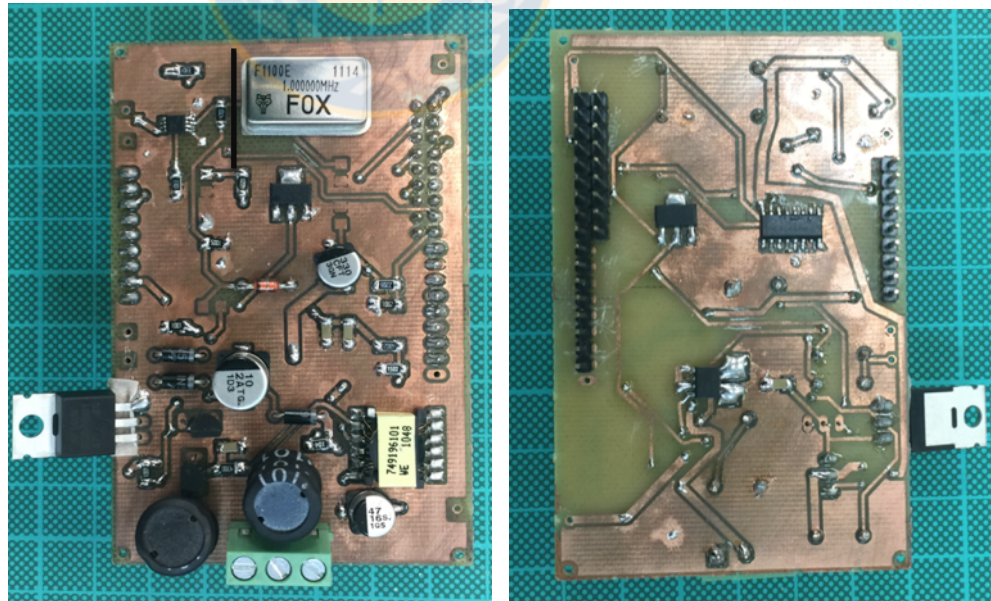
Tarjeta PCB diseñada, a) Parte superior, b) parte inferior. Fuente: Elaboración propia.
